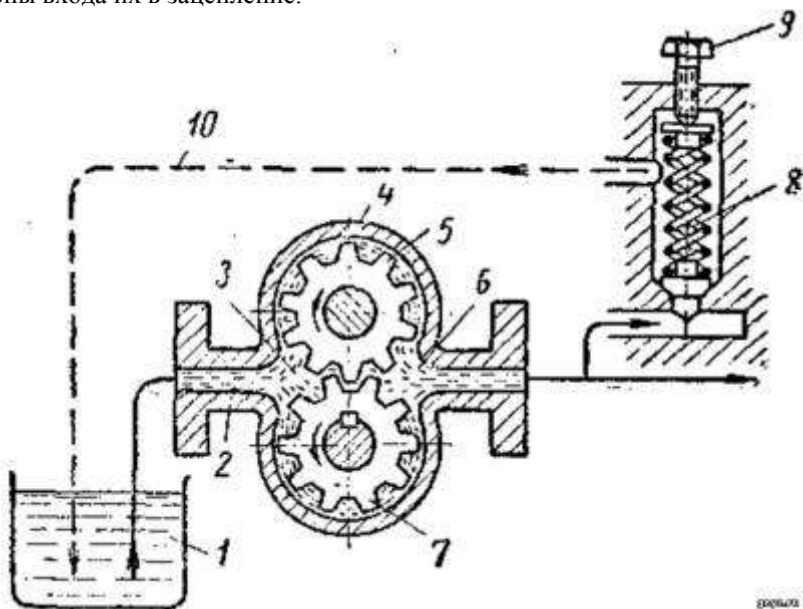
Схема установки шестеренчатого насоса: 1 — масляный бак; 2 — приемный патрубок; 3 — всасывающая полость; 4 — корпус; 5 — ведомая шестерня; 6 — нагнетательная полость; 7 — ведущая шестерня; 8 — перепускной клапан; 9 — регулировочный винт клапана; 10 — сливной маслопровод.
